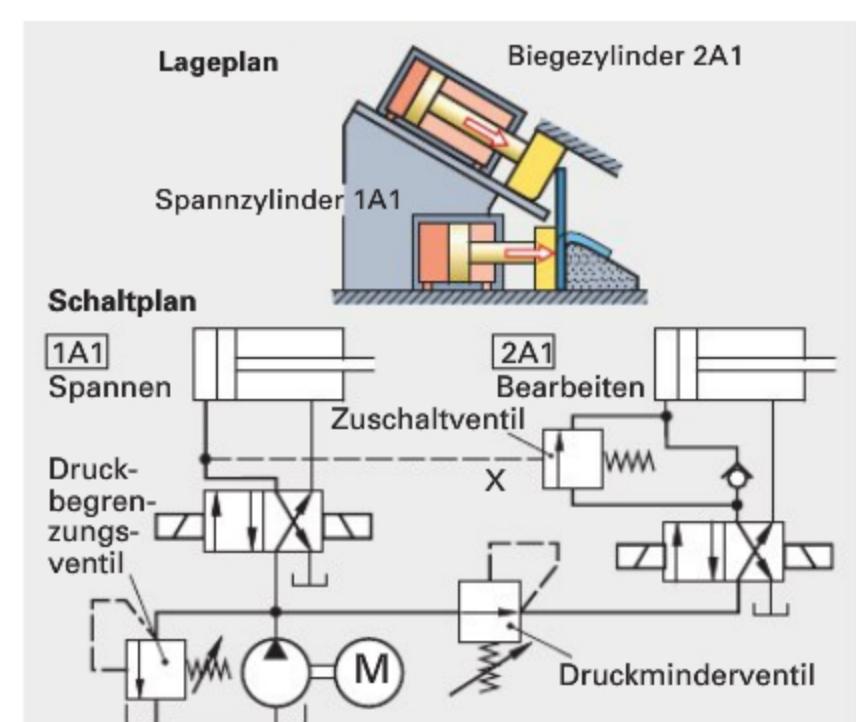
Druckventile in der Steuerung einer hydraulischen Biegevorrichtung
